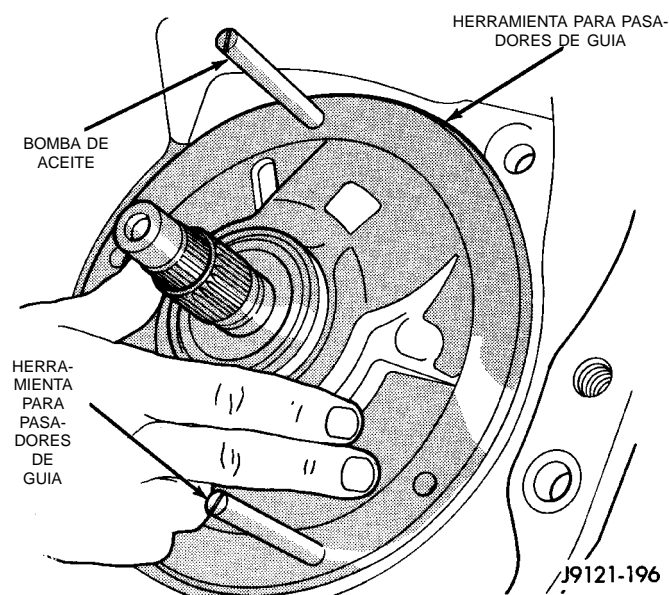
Instalación del conjunto de la bomba de aceite en la caja
